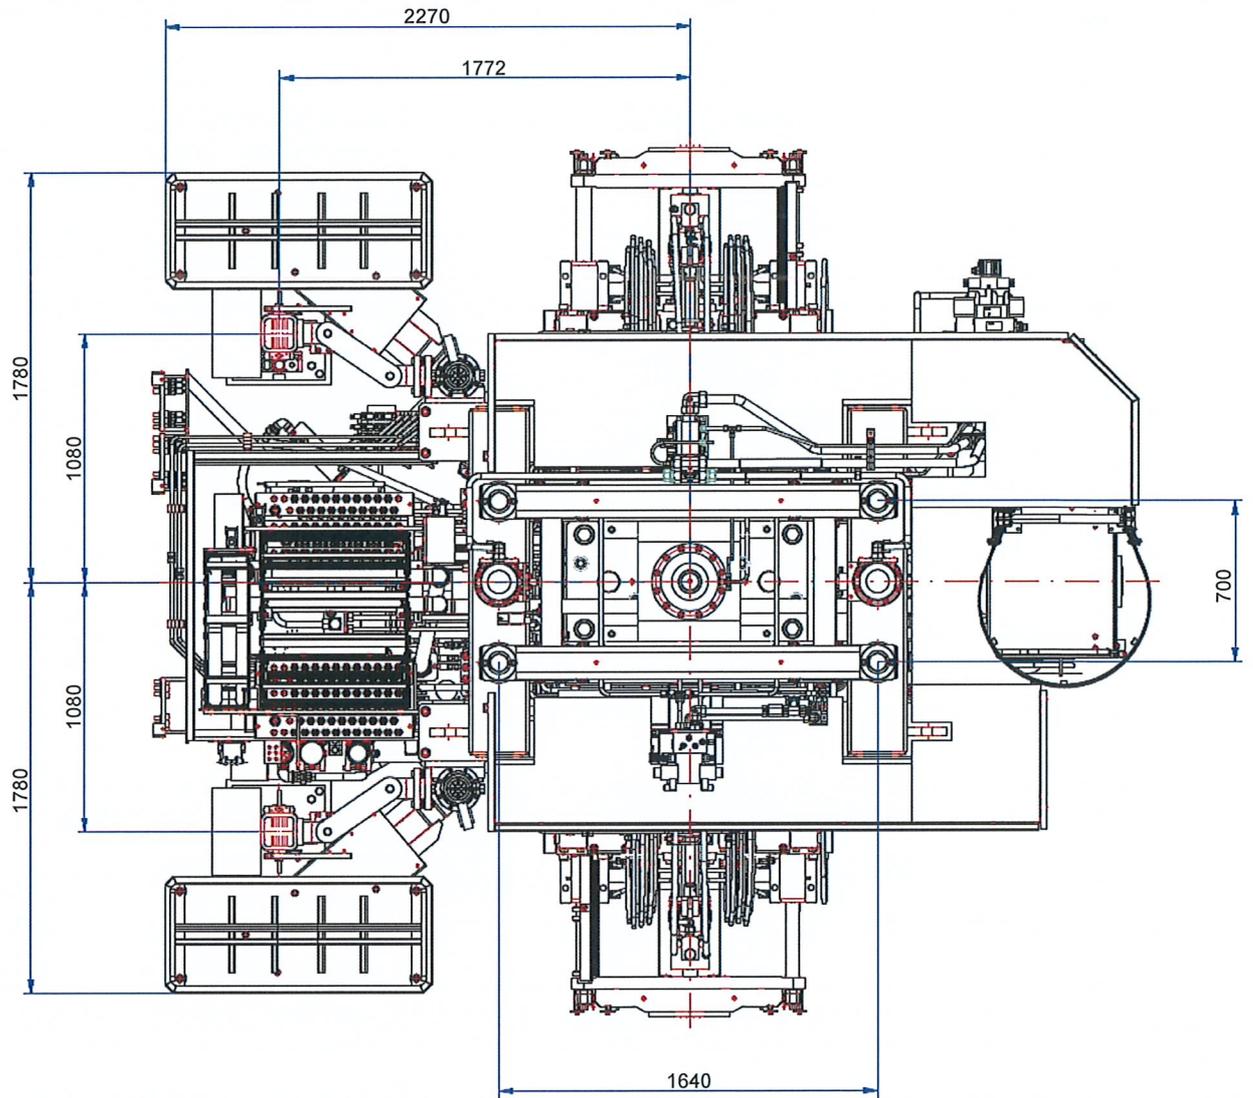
Maschinenlayout mit Gußteilentnahme - Draufsicht
